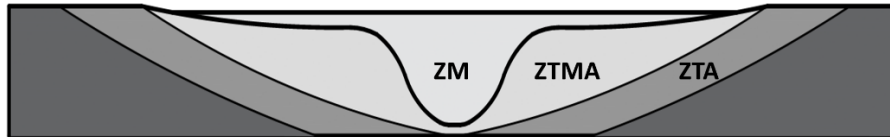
Seção transversal esquemática de soldagem por FSW [Autor].
